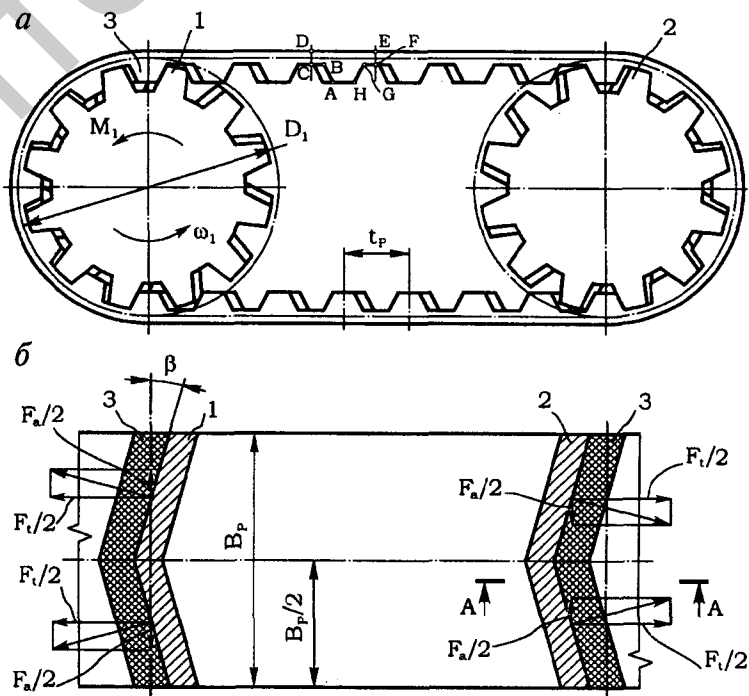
Внешний вид (а) и схема действия сил (б) в зубчато-ременной передаче с непрямыми зубьями: 1, 2 — шкивы, 3 — зубчатый ремень
